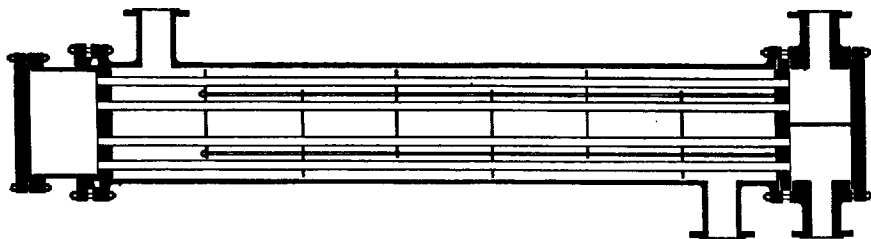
Intercambiador 1-2 de cabeza flotante empacada. (*Patterson Foundry & Machine Co.*)
